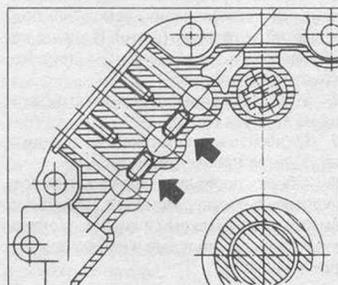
Расположение штифта блокировки (Глава 8)
